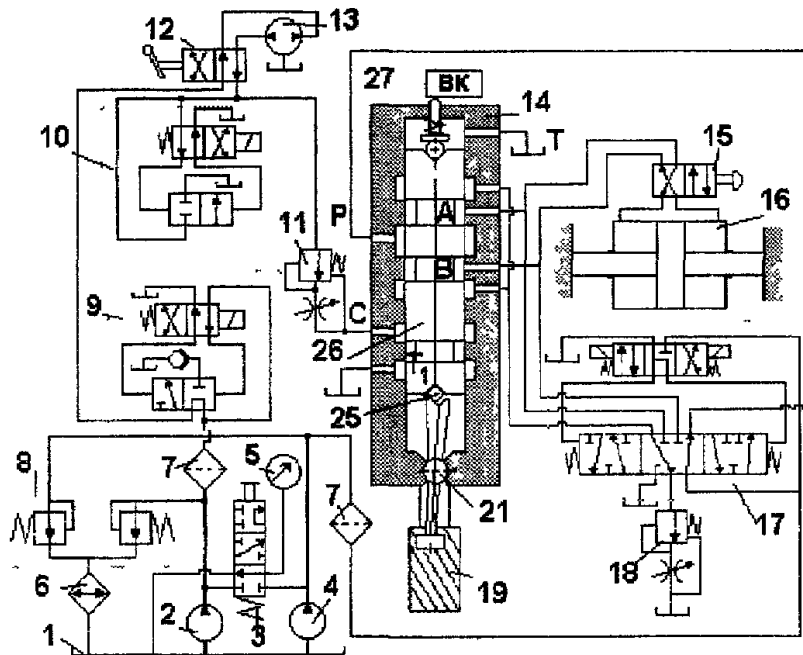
Гідралічна схема вертикально-фрезерного верстата
